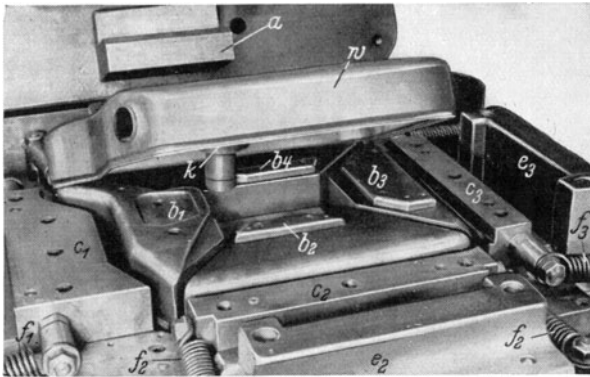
Spreizwerkzeug zum Hohlprägen einer umlaufenden Sicke in Kraftstoffbehälter-Hälften
